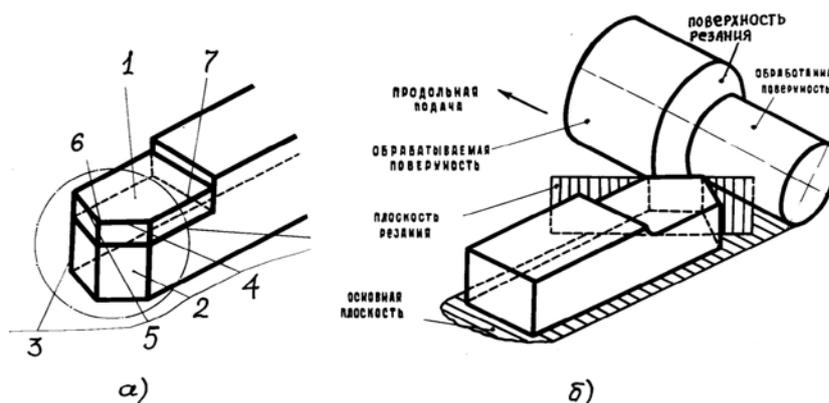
Элементы головки токарного проходного резца (а) и поверхности (б) при точении
